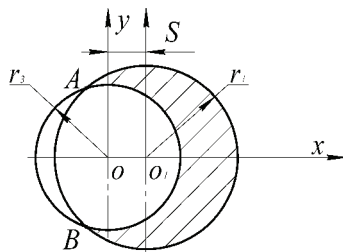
Схема взаємодії інструмента з деталлю при пружному відновленні відбитка
